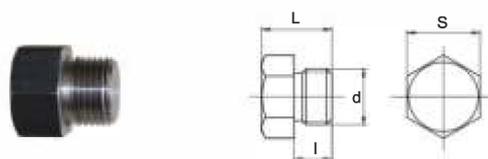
Заглушка для установки в муфту СДУ-ПК
